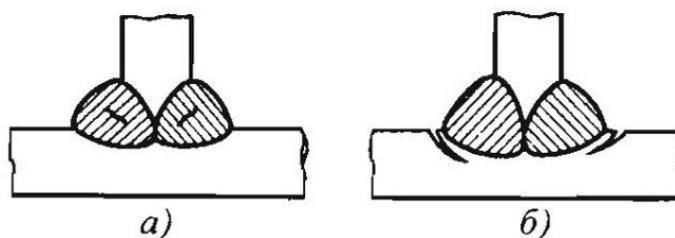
Трещины в сварных швах и соединениях: а – в наплавленном металле; б – в зонах оплавления и термического влияния
